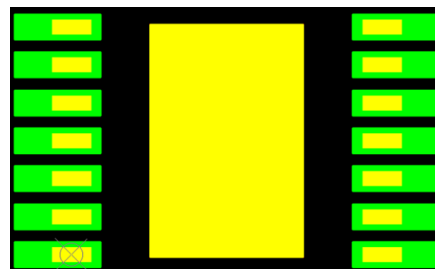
PWP0014L PCB 焊盘上的 SO-14，黄色：其他 SO-14 引线，绿色：TI PWP0014L PCB 焊盘
